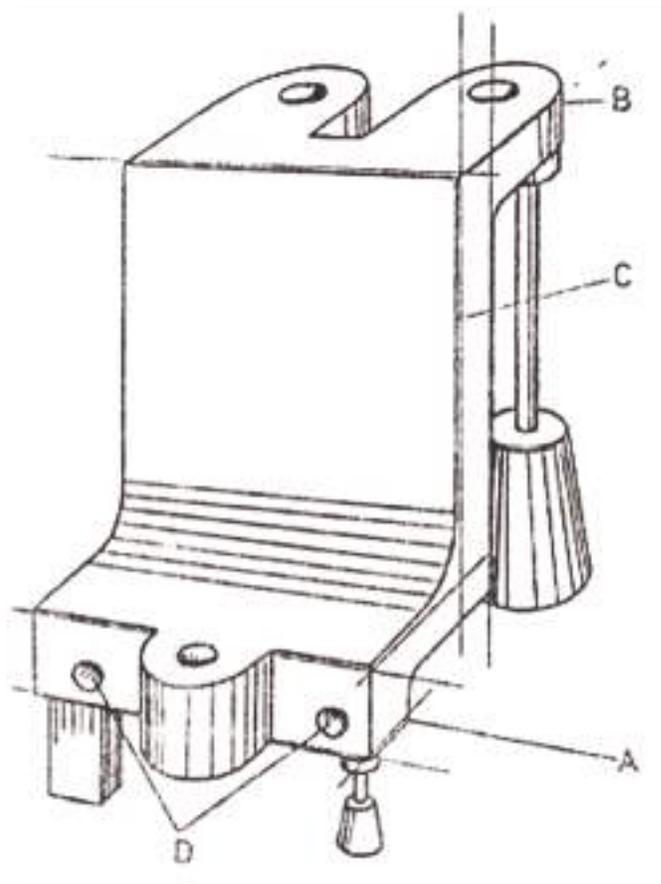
Colocação da peça para a traçagem de planos verticais perpendiculares ao plano já obtido (A e B são perpendiculares a C).
